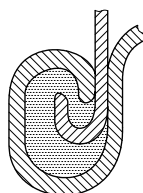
Assemblage à joint agrafé avec masse de remplissage
